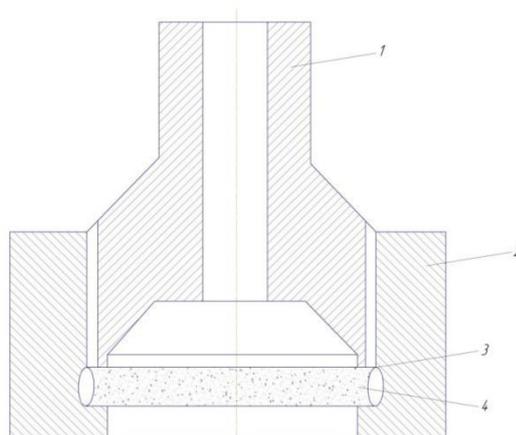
Приспособление для испытания на разрыв дисковых образцов
